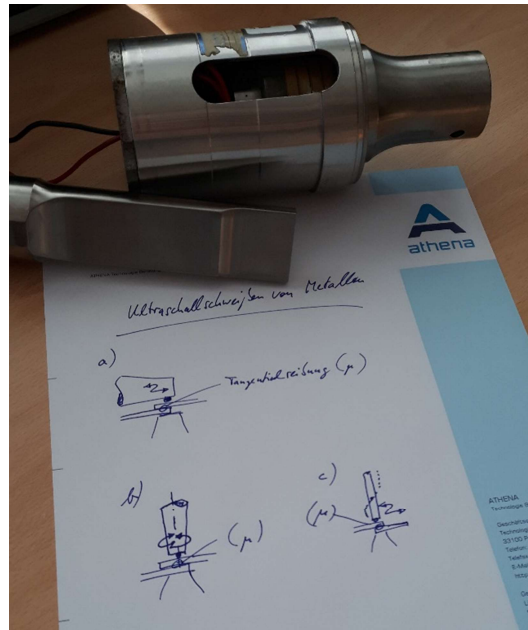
Schwingungskonzepte für das Ultraschallschweißen von Metallen: a) Längsschwinger mit seitlicher Schallauskopplung, b) Torsion, c) Biegung
